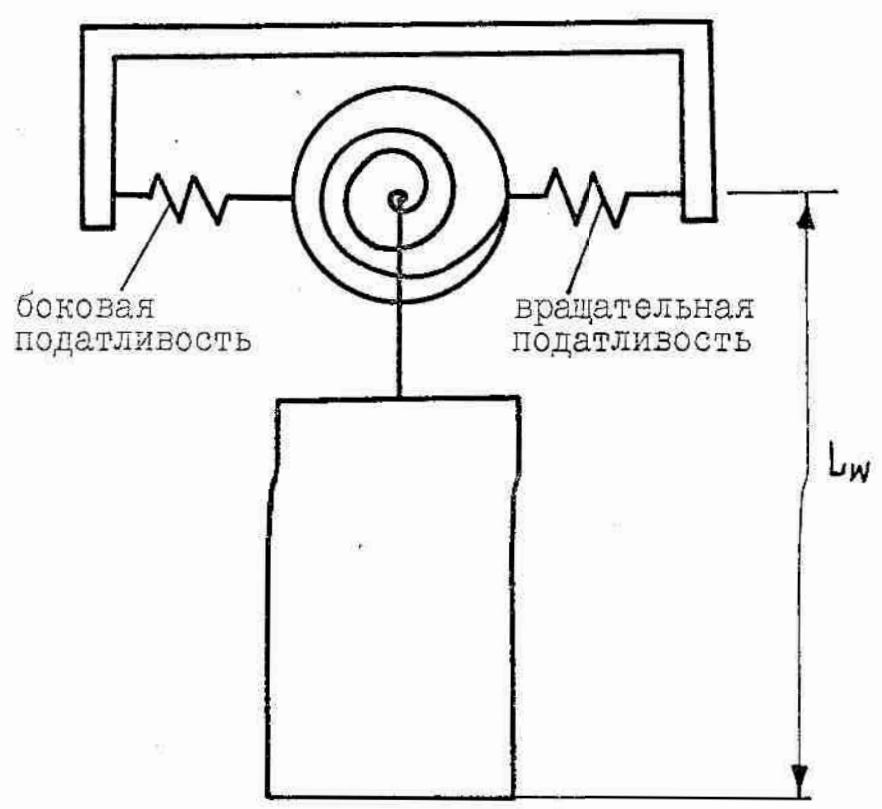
Схематическое размещение упругого устройства в схвате сборочной машины
